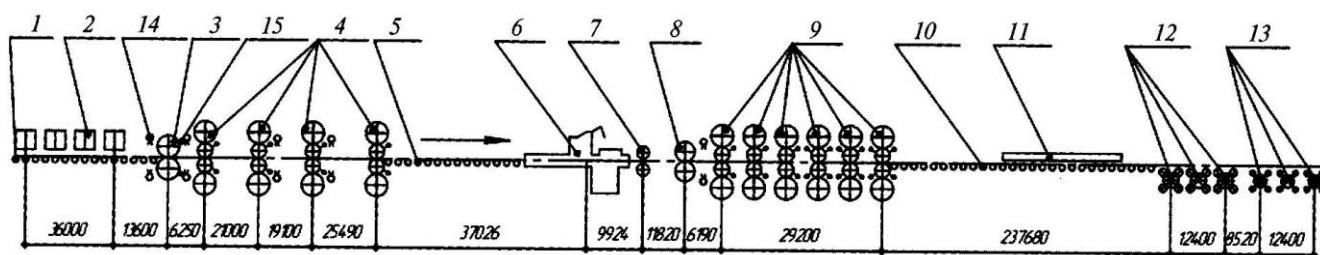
Схема розташування обладнання безперервного стану гарячої прокатки 1680 ПрАТ «Запоріжсталь»:
